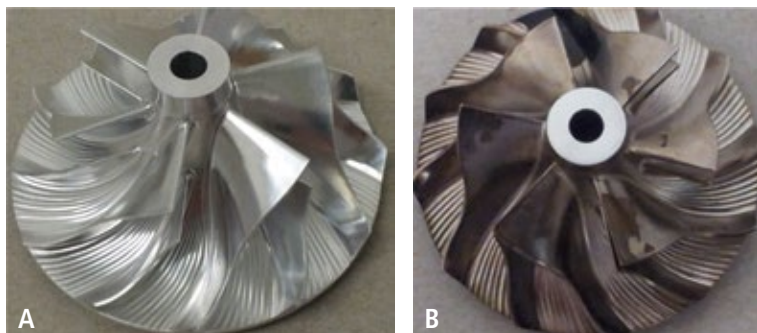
Beispiel für ein blankes (A) und ein beschichtetes Verdichterrad (B)
